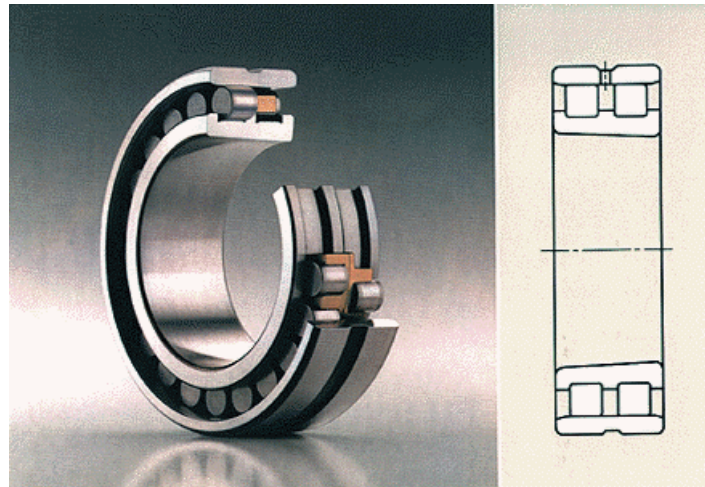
Rodamiento de rodillos cilíndricos de dos
